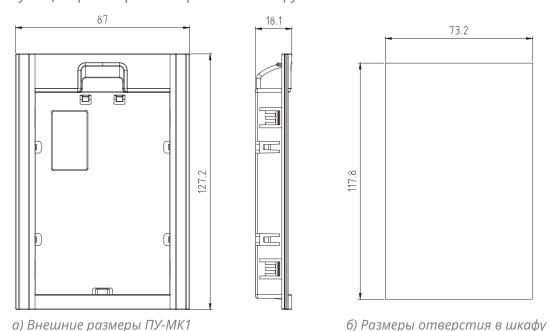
Внешние размеры ПУ-МК1 и размеры отверстия в шкафу
